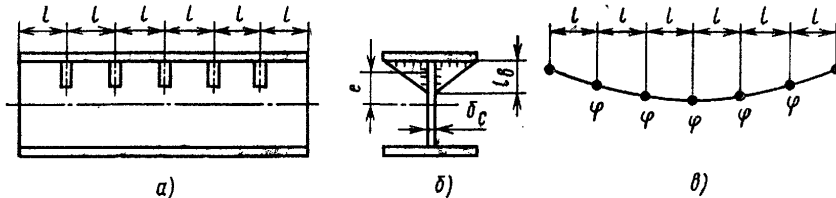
Схемы изгиба балки, имеющей ребра, приваренные к вертикальной стенке и верхнему поясу
